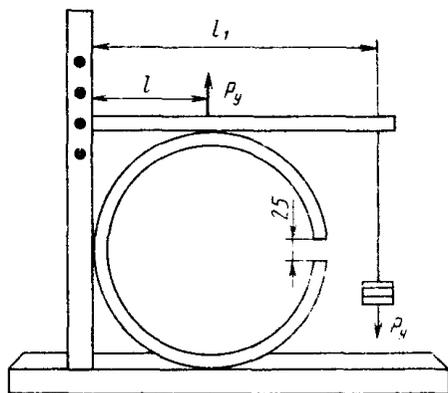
Схема приспособления для проверки упругости поршневых колец
